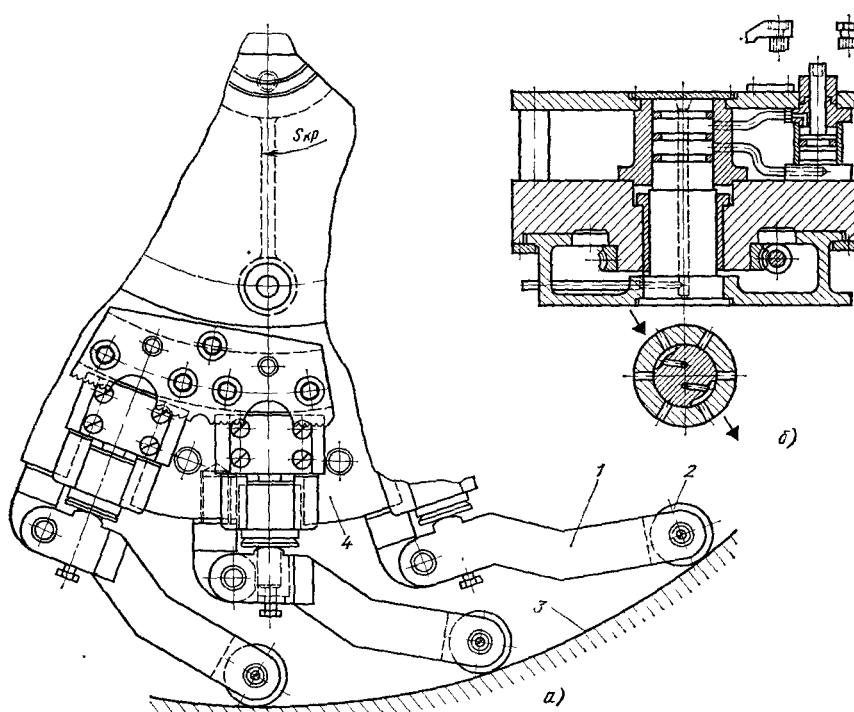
Зажимной механизм приспособлений к станкам непрерывного действия
